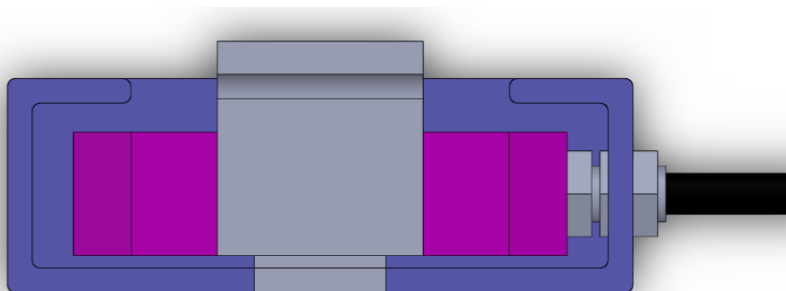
Vista en planta de del sistema de sujeción de la célula.
